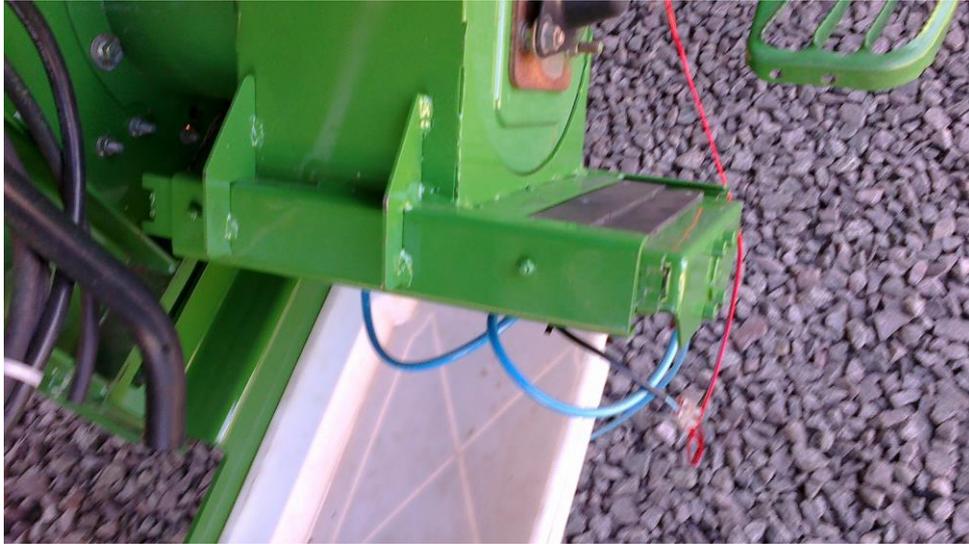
Conjunto ponteadado por solda e montado na colhedora
